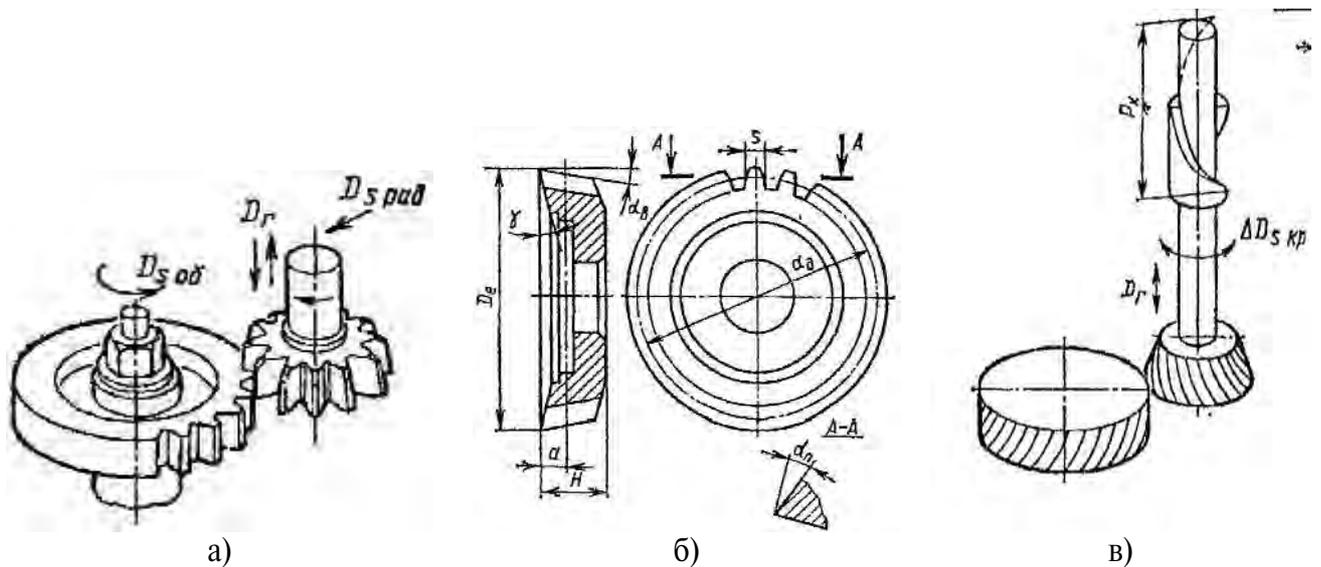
Схемы работы и конструкции зуборезных долбяков
